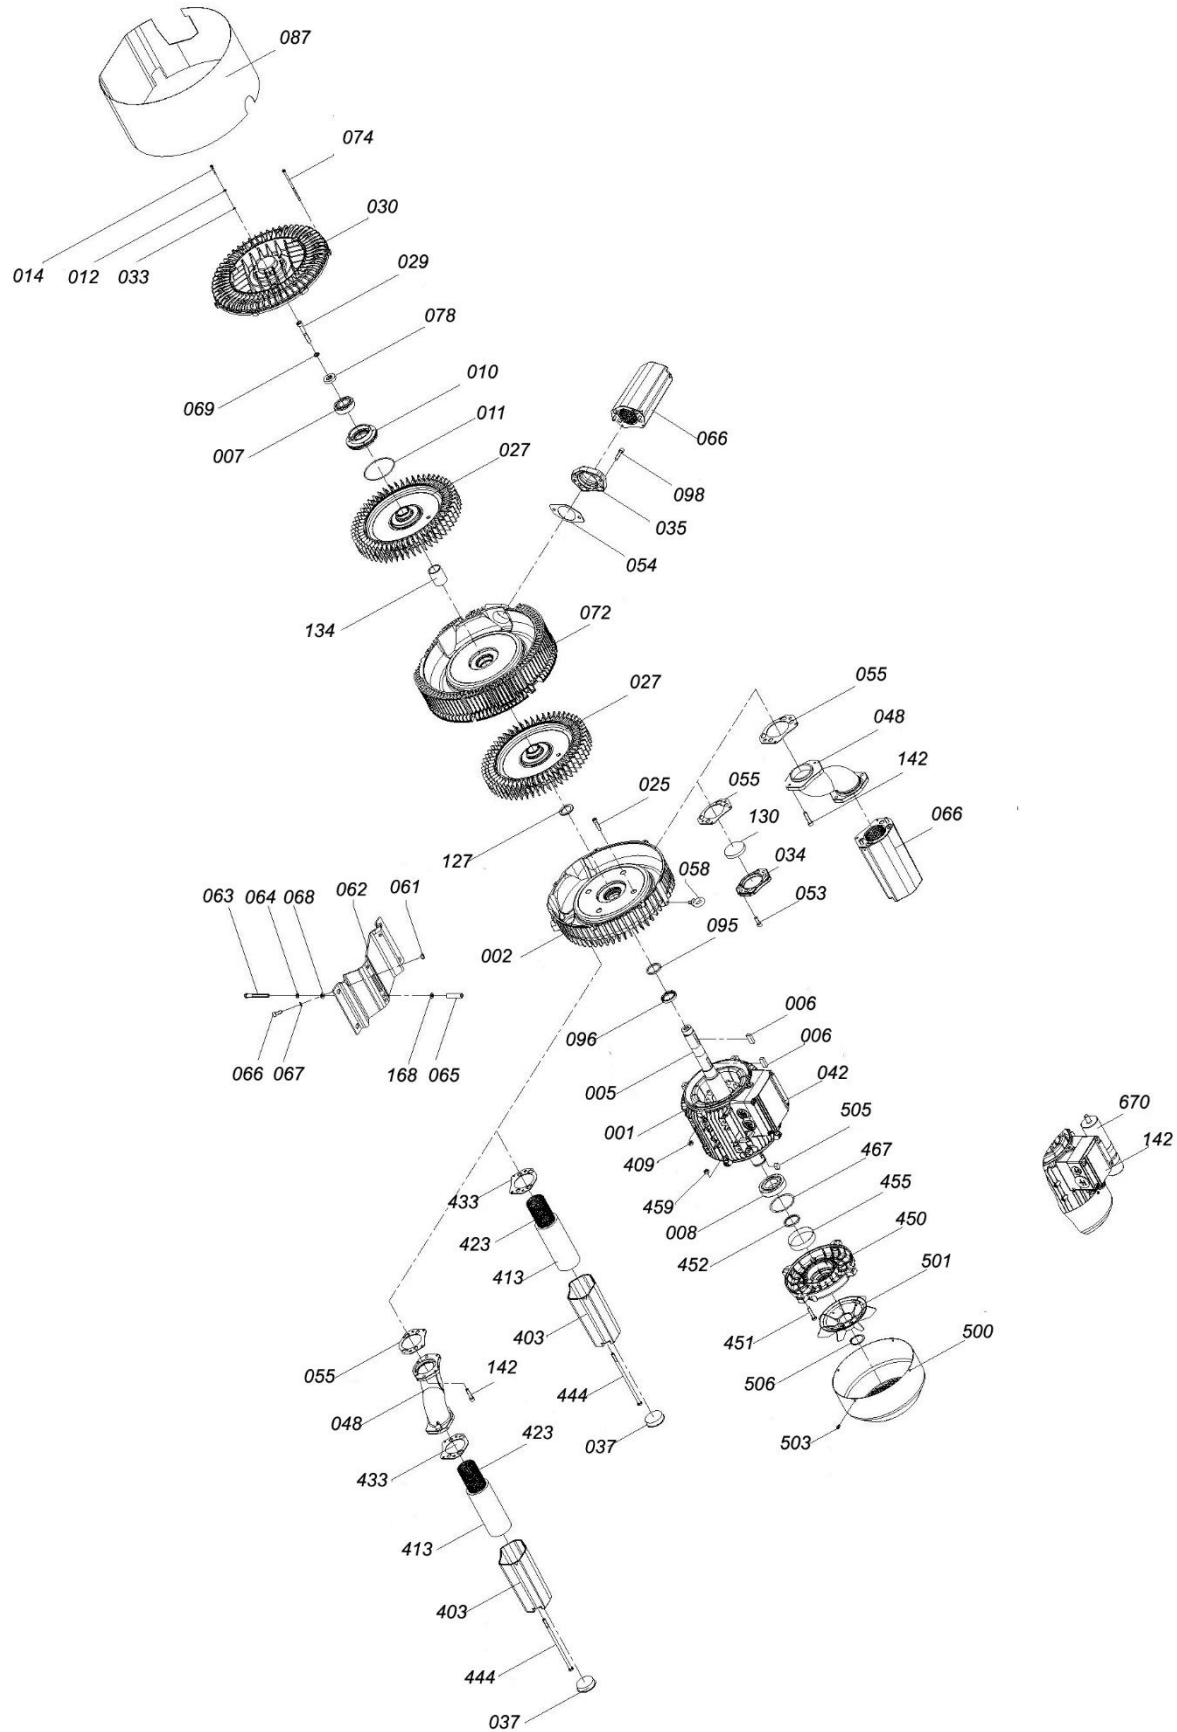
Деталировка двухступенчатых воздуходувок 2RB
